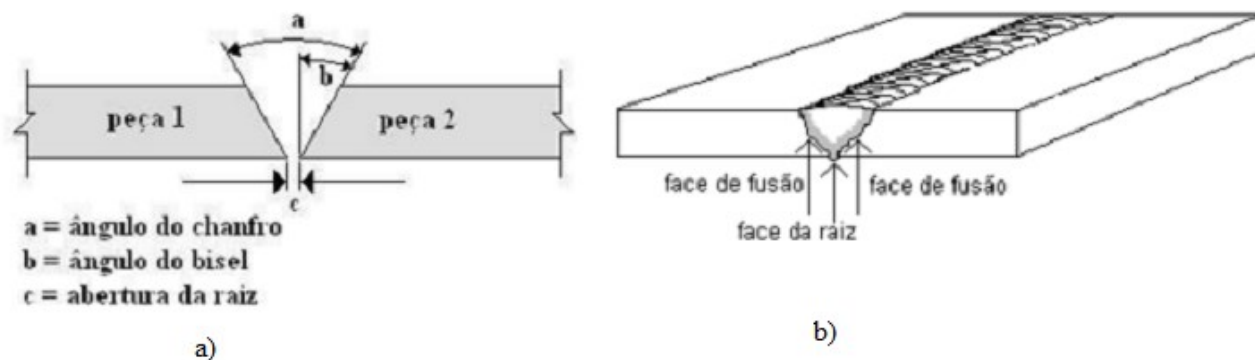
a) dimensões de uma junta soldada tipo V. b) Zona de fusão da solda para uma junta tipo V.
